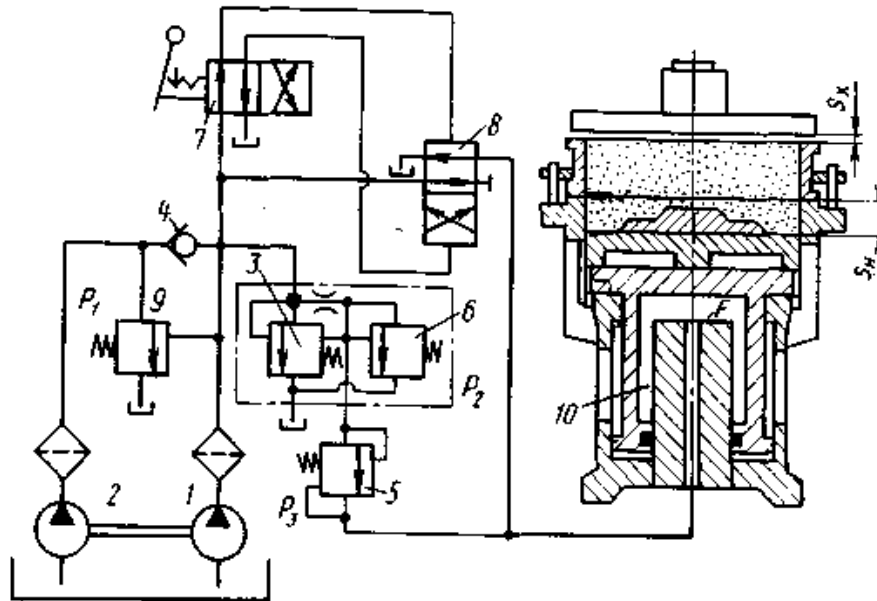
Гидропривод прессовой формовочной машины с нижним прессованием
